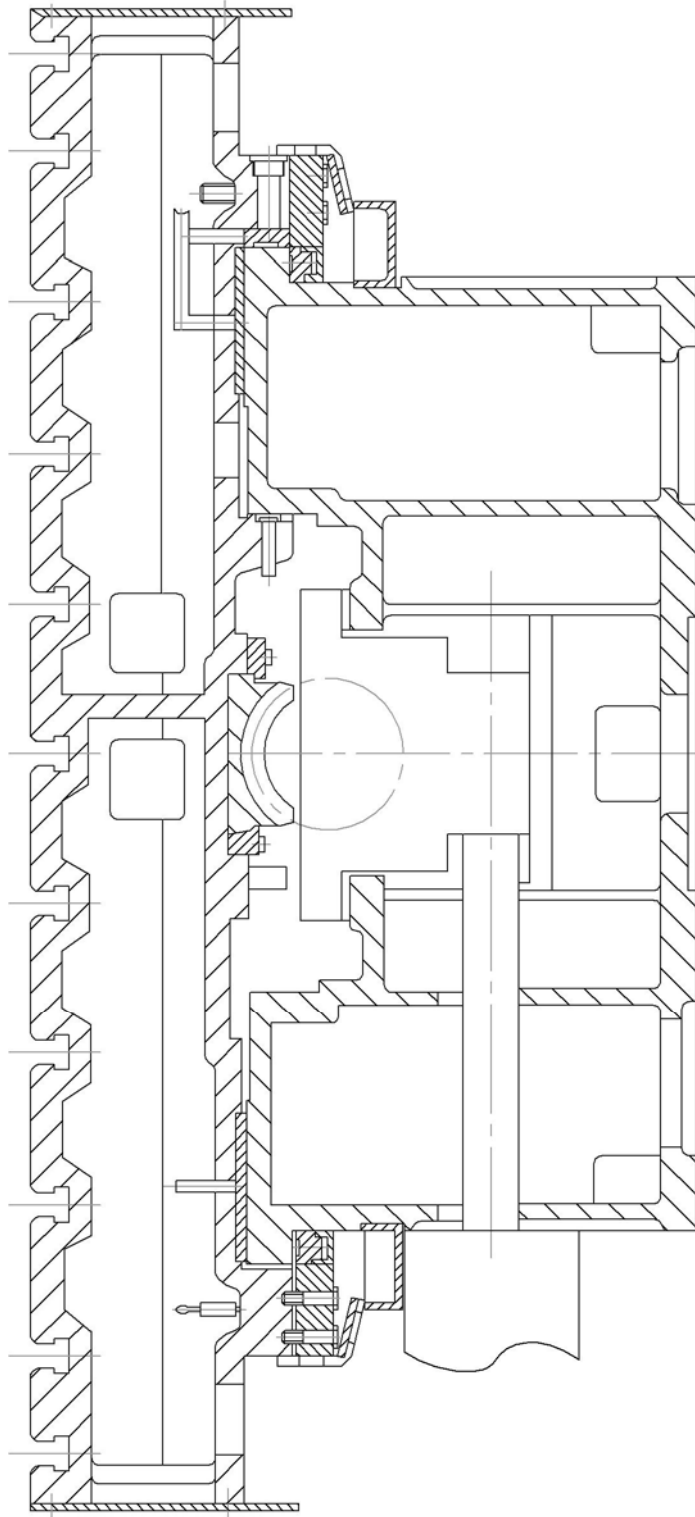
Пояснить основные особенности направляющих продольно-фрезерного станка с ЧПУ
